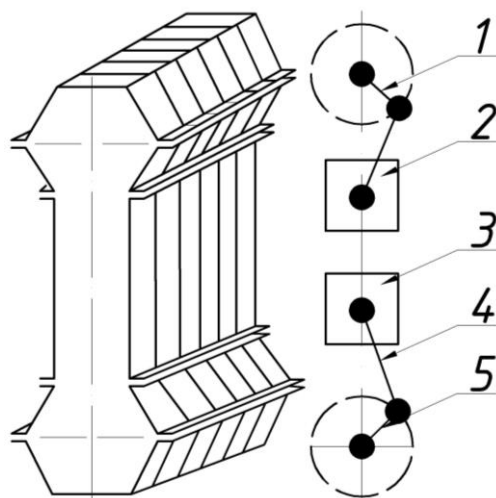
Расположение цилиндров рядного двигателя 2Д100
